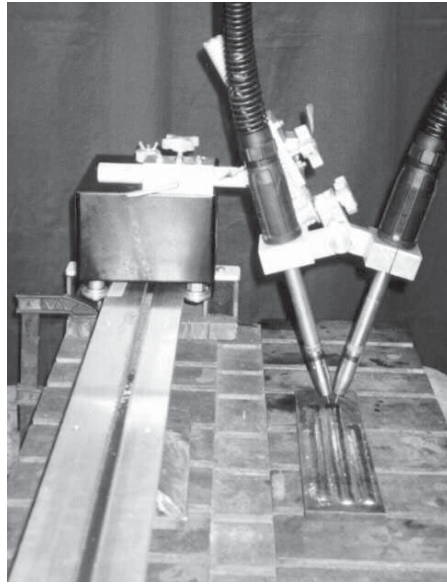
Posicionamento “lado a lado” dos eletrodos para a realização das soldagens.
